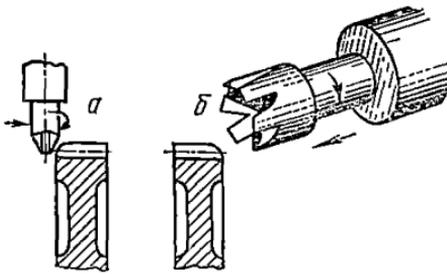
Обработка закруглений, скосов и фасок на торцах зубьев: *а* — пальцевой фрезой; *б* — полый фрезой.
